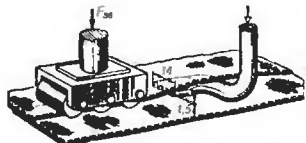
Схема механізованого неперервного зварювання шлівки газовим теплоносієм
